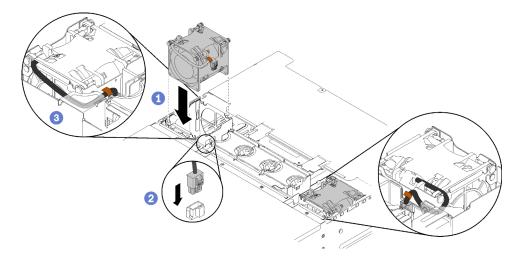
Instalação do ventilador de 80 mm x 80 mm x 80 mm
